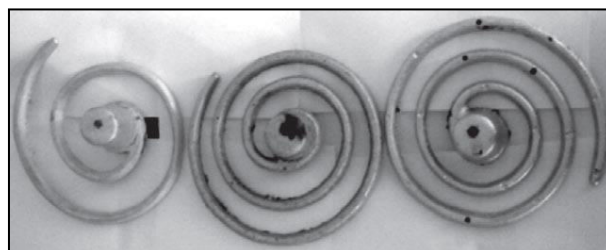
Vzorky získané ze zkoušky DI, Straube – Pfeiffer Test a Dross Test [18]
